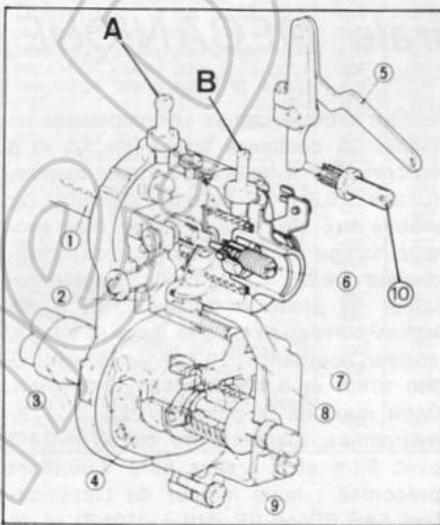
Vue en coupe du régulateur de la pompe d'injection - 1, crémaillère - 2, membrane de l'élément pneumatique - 3, arbre à cames - 4, masselotte - 5, levier de commande d'accélération - 6, vis de butée de ralenti - 7, ressort de rappel de la membrane de l'élément pneumatique - 8, fourchette de liaison - 9, ressort de rappel de l'élément mécanique centrifuge - 10, vis de réglage d'émission de fumée - A, raccord de prise de dépression en amont du papillon - B, raccord de dépression en aval du papillon.
